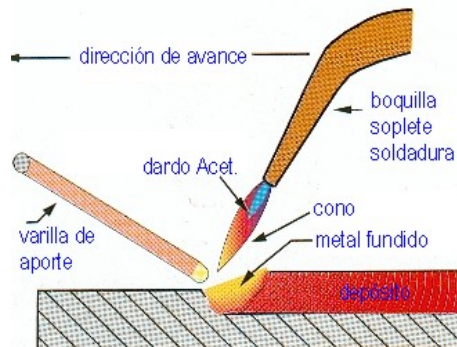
Soldadura Oxiacetilénica.
